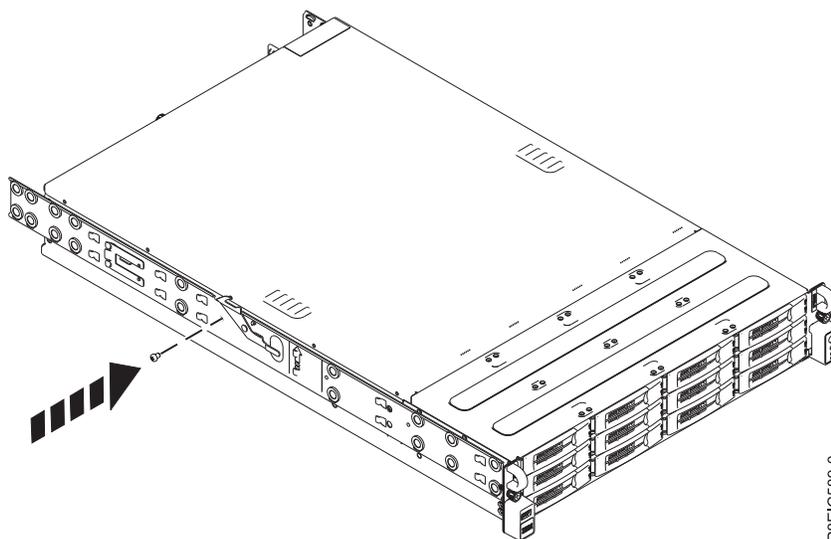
Sicherungsschraube der linken Schiene des Systemchassis am Systemchassis anbringen
